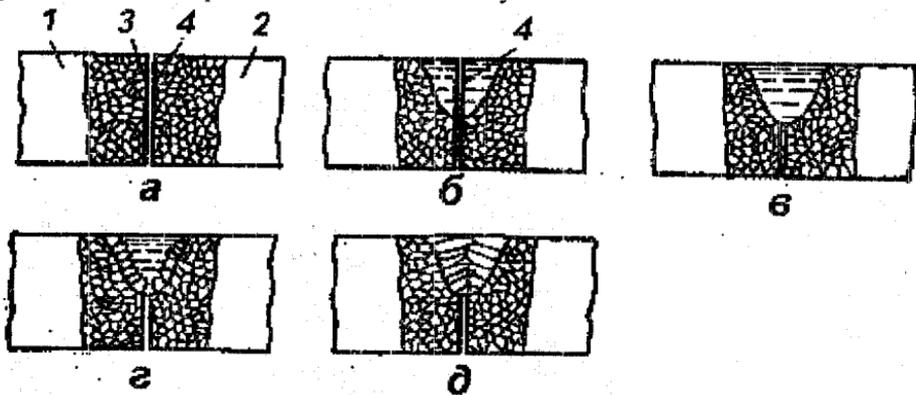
Схема процесу утворення зварного з'єднання шляхом плавлення:
